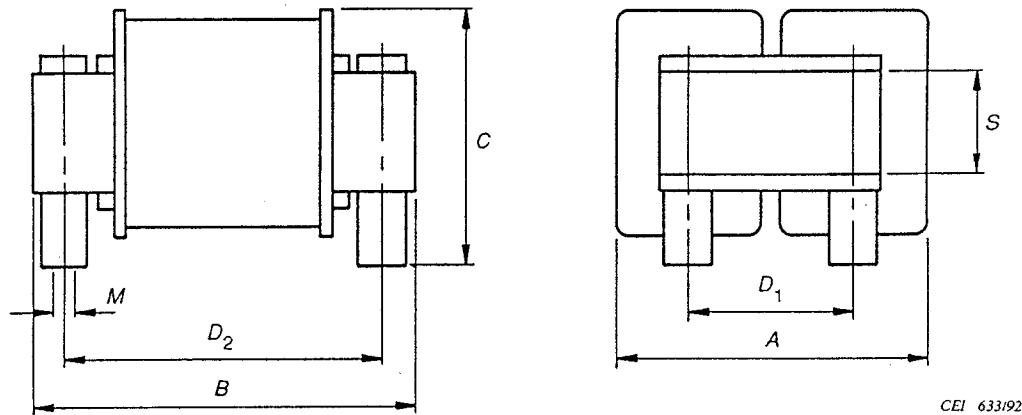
Mode de montage horizontal pour transformateurs et inductances en tôles découpées YUI 1-10 à YUI 1-80 – montage sur montants
